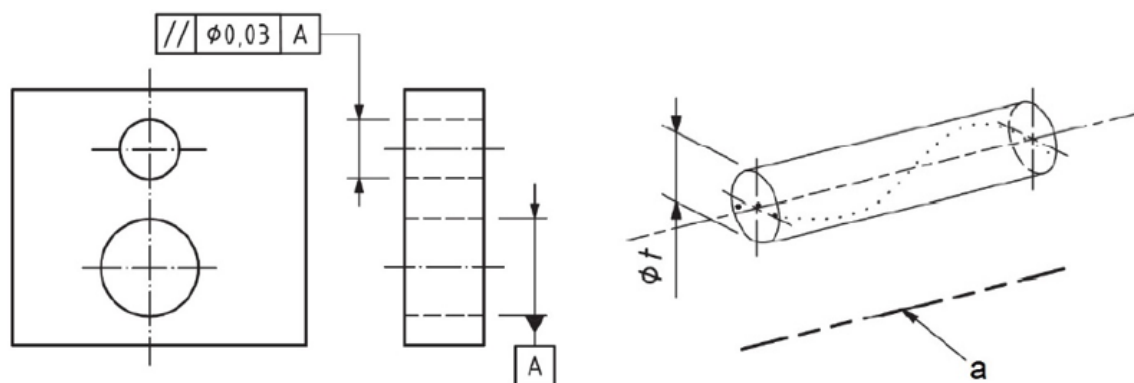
Indikátor kolmosti se základnou A a příslušné toleranční pole (1)
